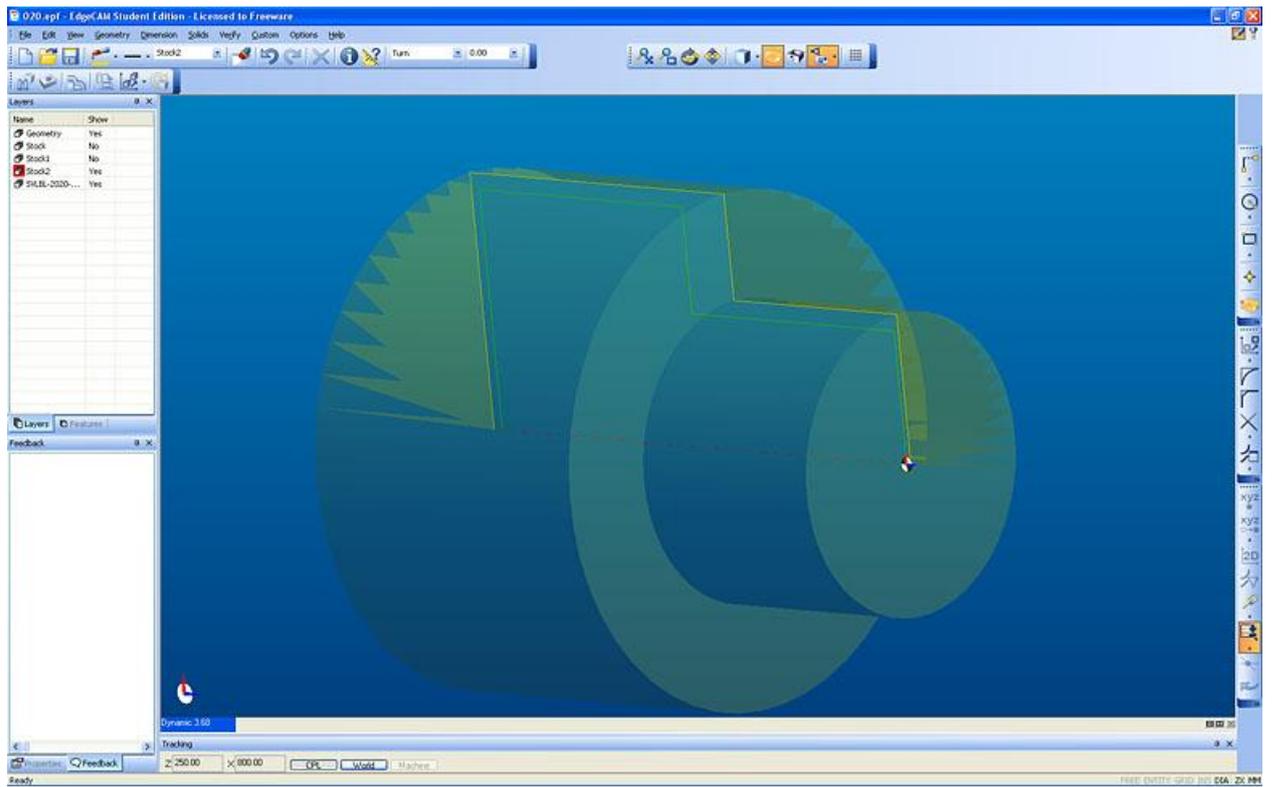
Edgecam. Создание заготовки для токарной обработки
